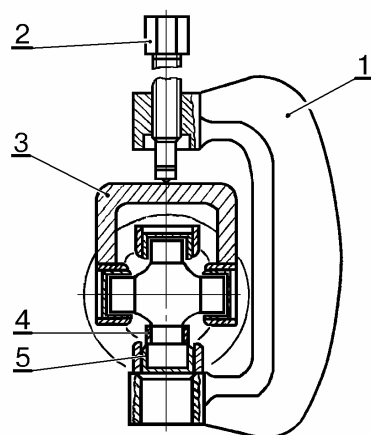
Выпрессовка подшипников крестовины 2105/21211-2202025.
